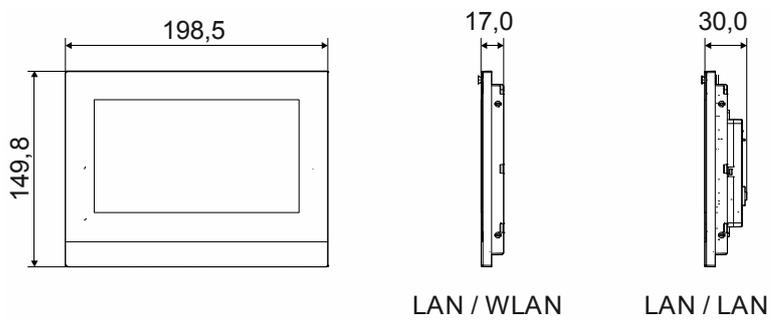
Außenmaße Innenstationen IP touch 7 (Maße in mm)
